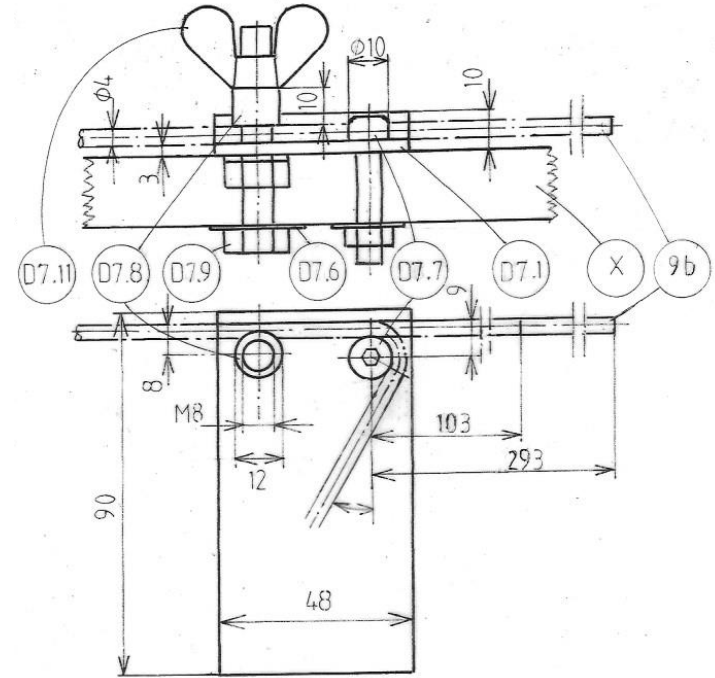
Dibujo del dispositivo D7 para doblar triángulo del recipiente (7), de acero (soporte soldado), o de aluminio o acero inoxidable (soporte con abrazaderas); diámetro: 4 mm
